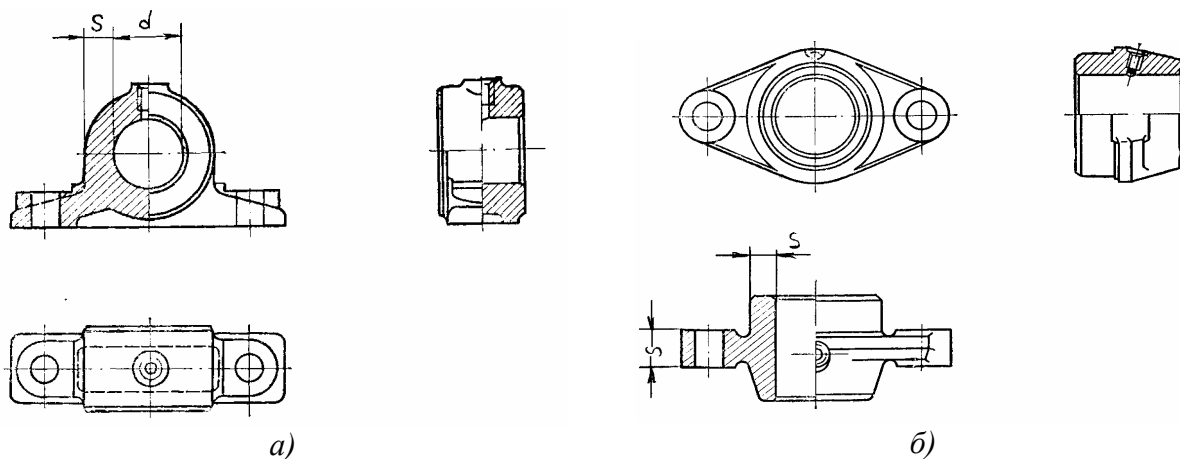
Конструкция неразъемных корпусов подшипников скольжения
